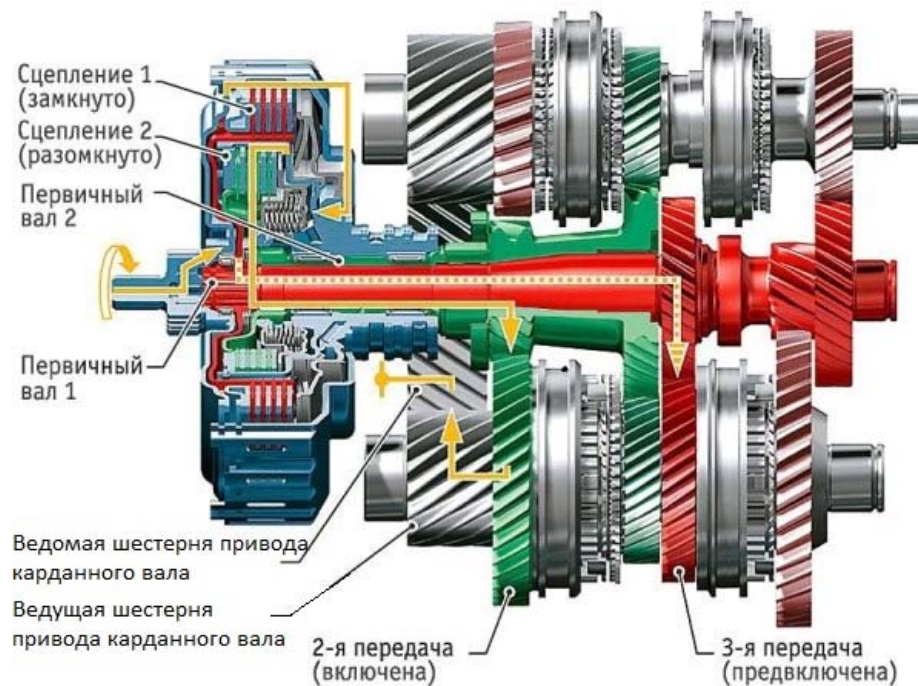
Схема коробки передач с двойным сцеплением [3]
